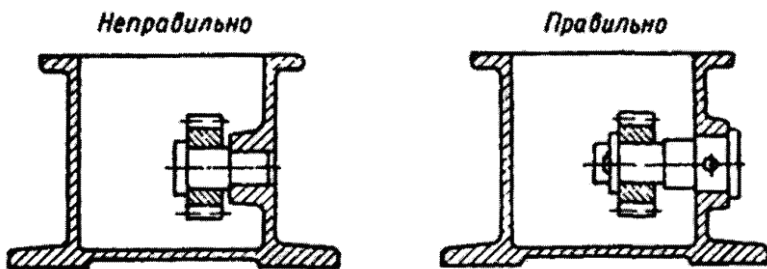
Конструктивні рішення корпуса редуктора
